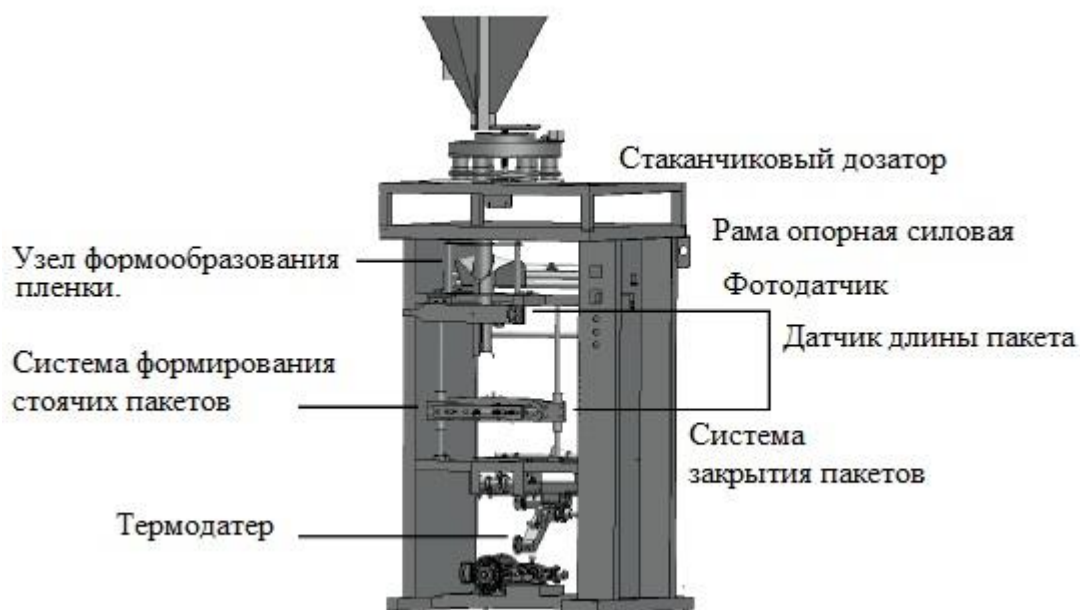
Пример фасовочно-упаковочного автомата со стаканчиковым дозатором.
